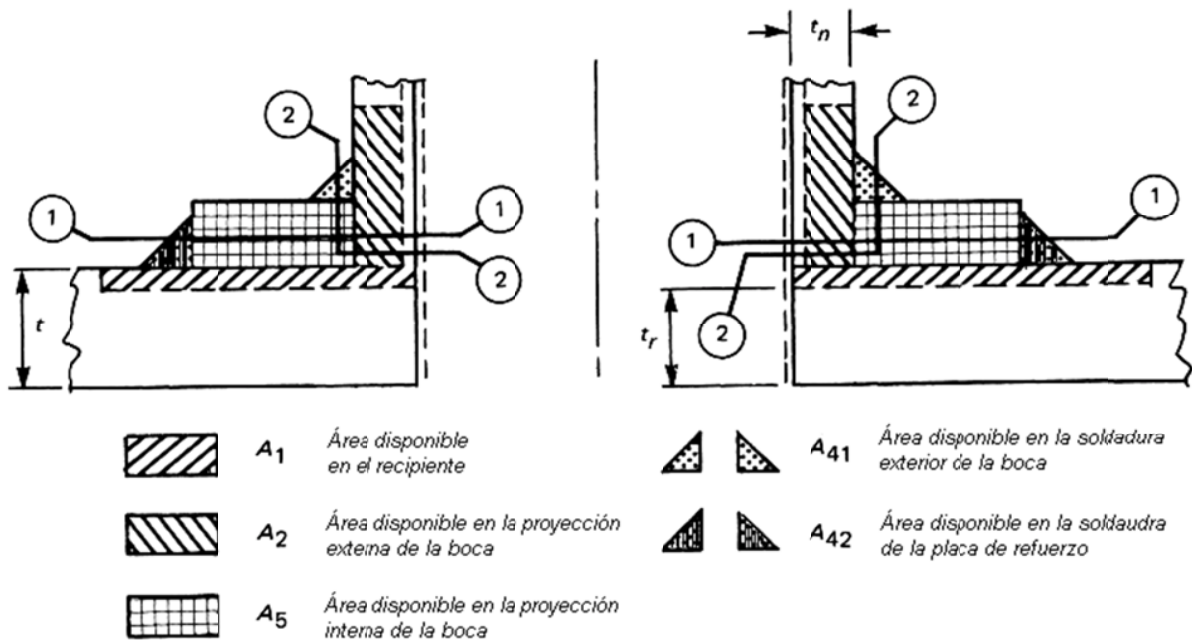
Cargas en las juntas de soldadura (bocas apoyadas)⁴⁸
